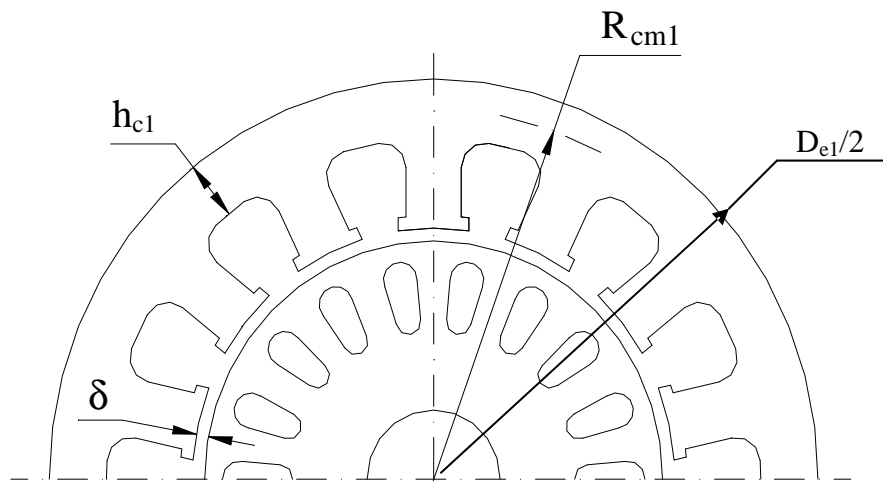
Desenho do estator e do rotor de um motor de indução.
